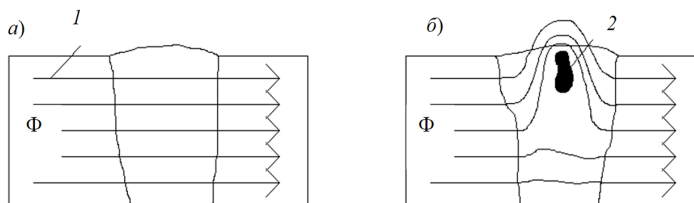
Схема прохождения магнитного потока в сварном соединении:
